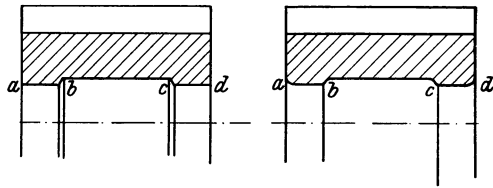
Falsch gedrehter und richtig gedrehter Fräser.
